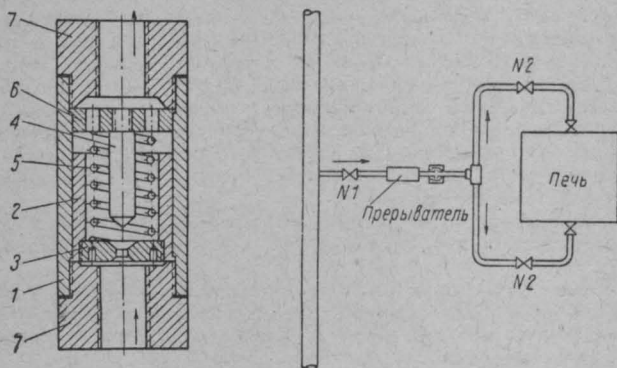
Прерыватель конструкции Нянькина и Круглова.
